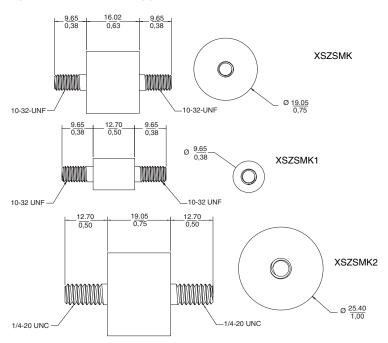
Dimensioni Kit di montaggio antivibranti (mm/in)
